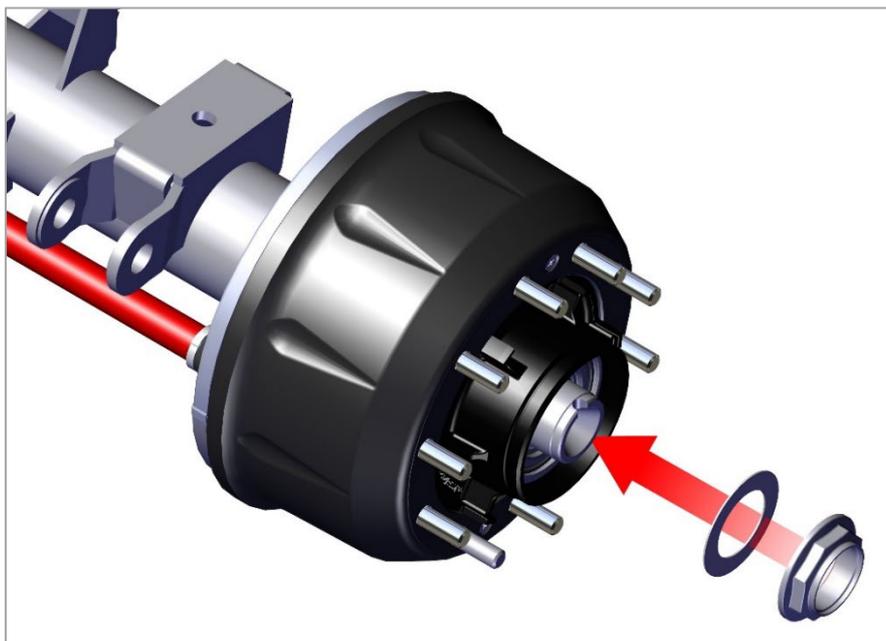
Монтаж упорной шайбы и гайки подшипников ступицы
